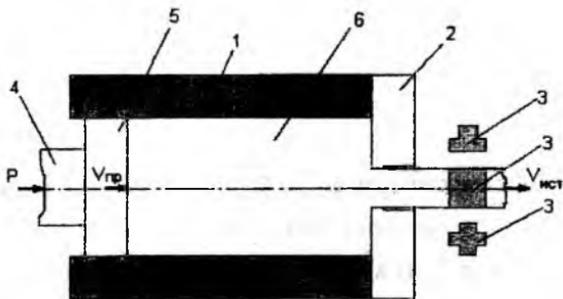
Схема прессования: 1 — контейнер; 2 - матрица; 3 - прессуемый профиль; 4 – пресс-штампель, 5 – пресс-шайба, 6 – заготовка
